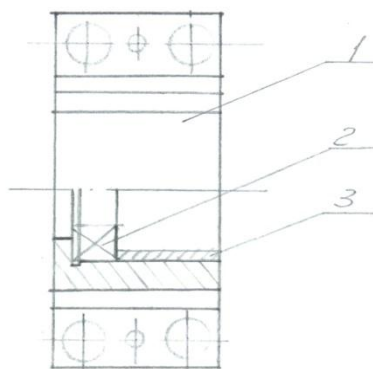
Схема практичного застосування корпуса 1 корпус 2 підшипник 3 втулка розпірна
